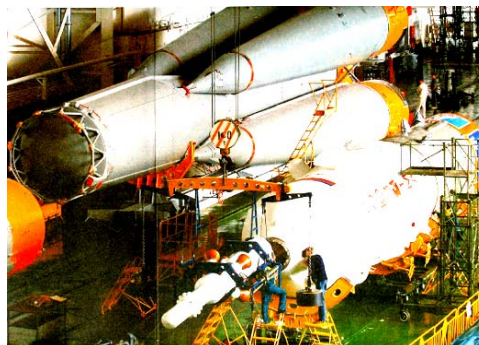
Внешний вид основных частей мощного советского трехступенчатого ракетносителя и транспортного космического корабля "Союз-ТМ" во время их сборки в монтажно-испытательном корпусе космодрома "Байконур" [8]
